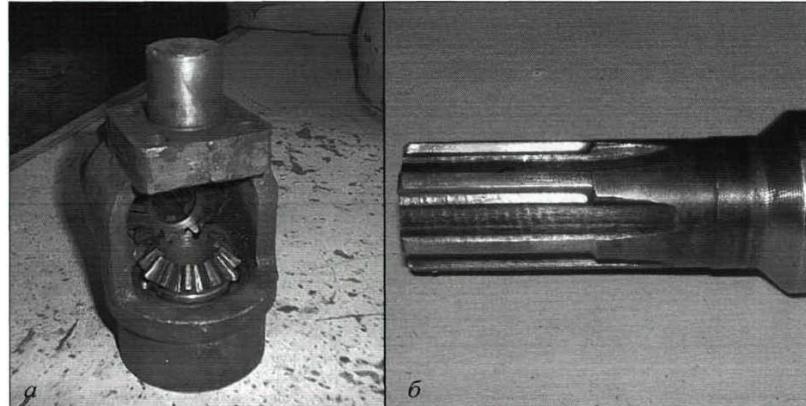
Конический редуктор механизма привода масляного насоса в сборе 700A.17.01.290 (а) и шлицевая часть вала привода насоса 700A.17.01.191 (б)
